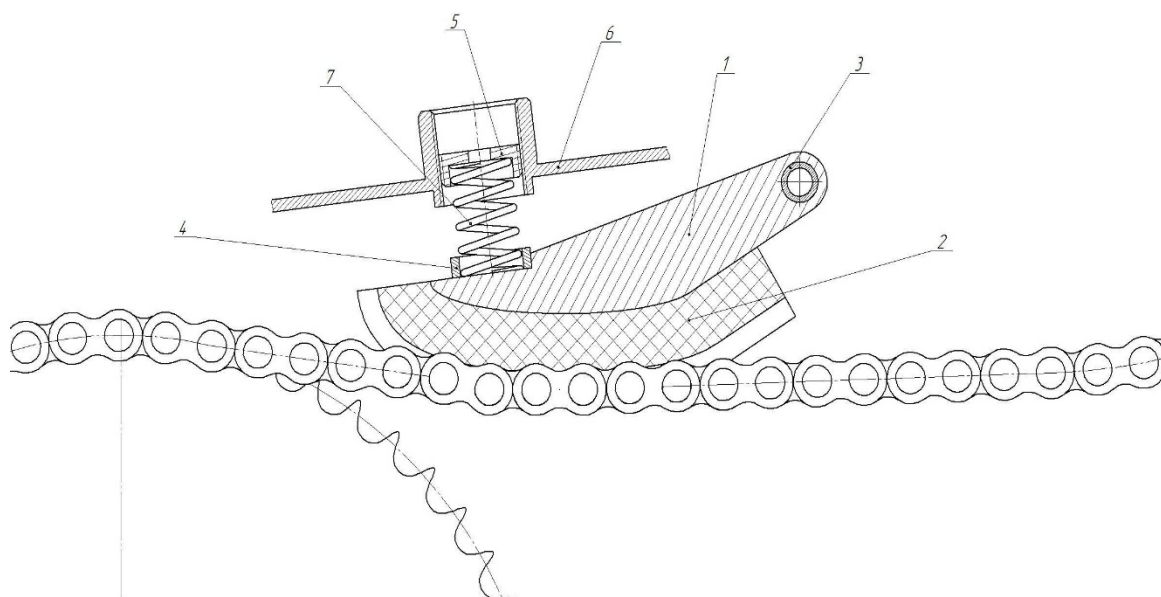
Натяжитель цепи: 1-корпуса натяжителя; 2-накладки, контактирующей с цепью; 3-фиксирующей втулки натяжителя; 4- полого вала; 5- стакана, регулирующего натяг цепи; 6- корпуса балансира; 7-пружины сжатия
